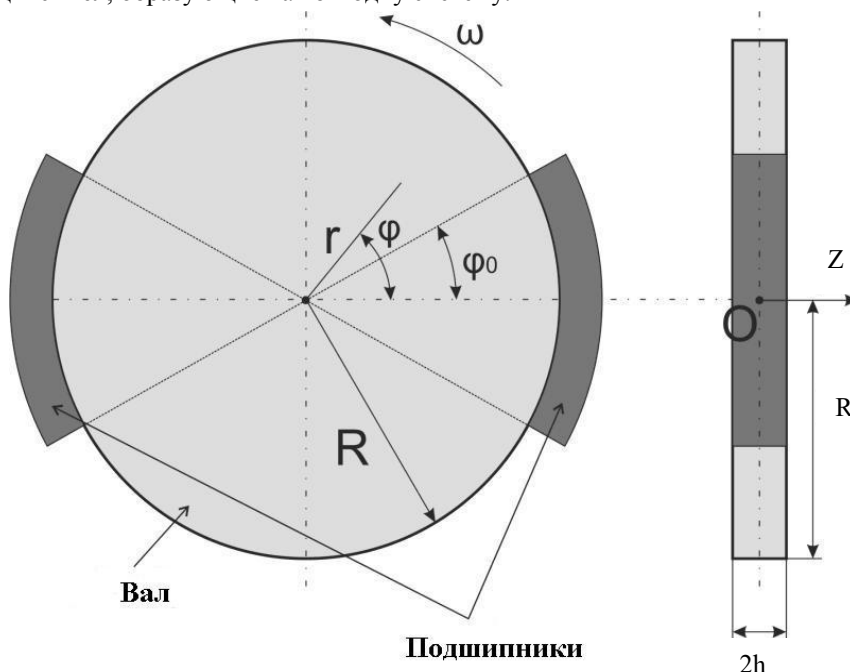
Схема металлополимерной трибосистемы "вал-частичный подшипник"
